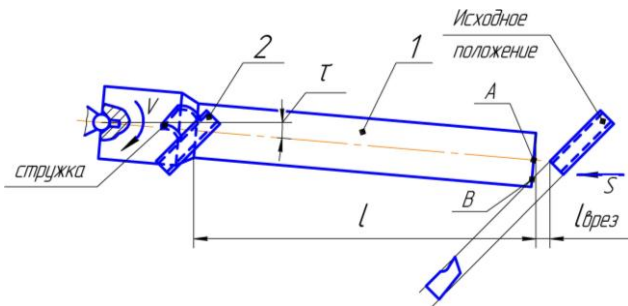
Схема обработки длинного вала проходным безвершинным сабельным резцом
